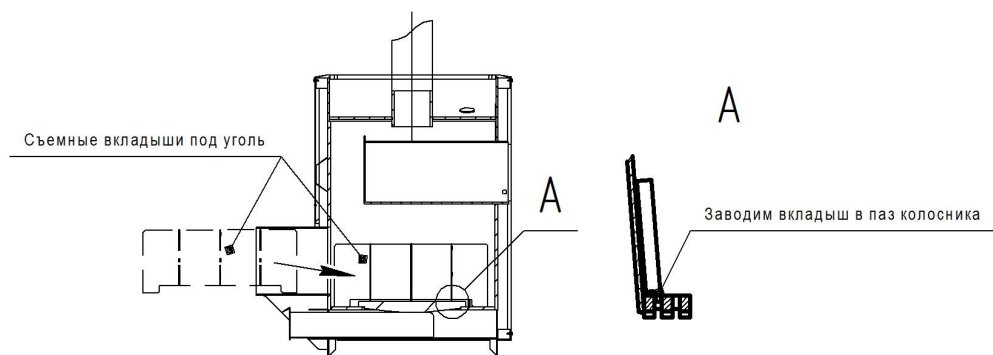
а - Установка боковых вкладышей под уголь в топку печи для бани
